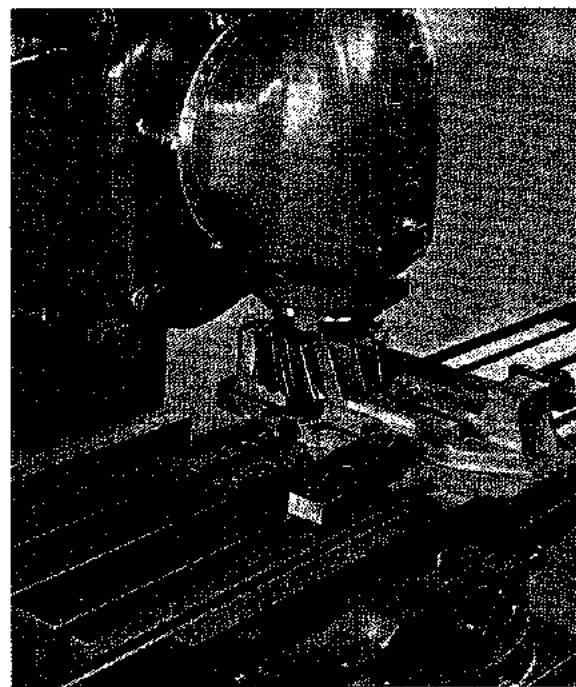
Accesorio de fresado vertical (Brown & Sharpe Mfg. Co.)
